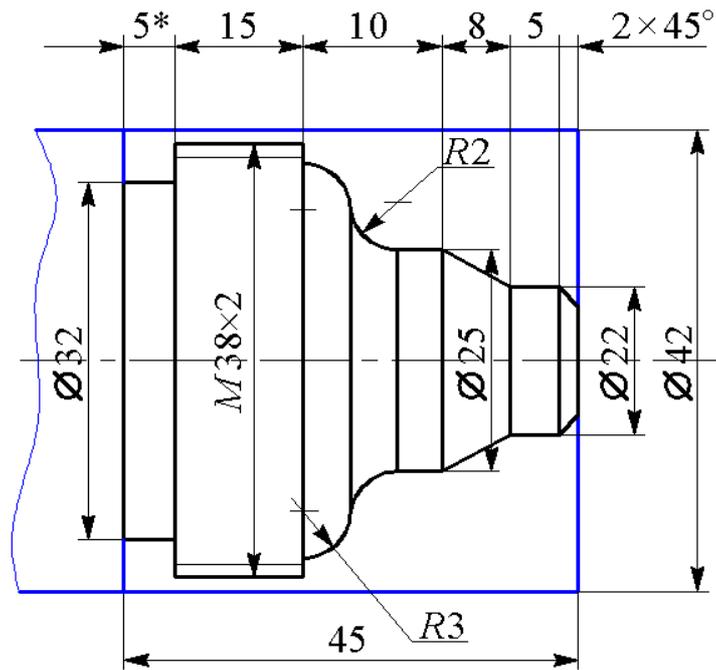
Эскиз обрабатываемой детали для подгруппы 1
